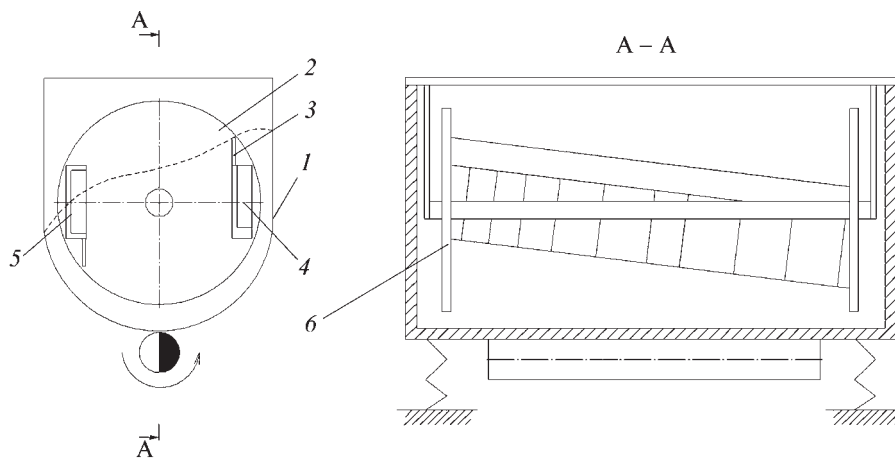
Схема работы приспособления с дополнительными лопастями:
